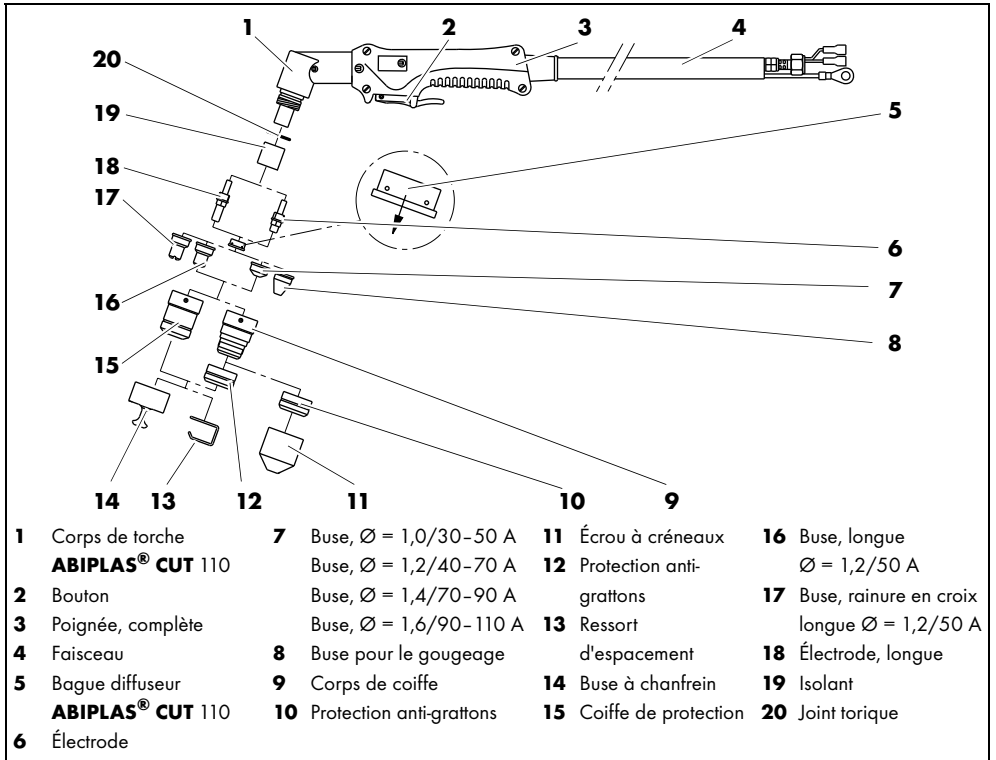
Vue d'ensemble de ABIPLAS® CUT 110
